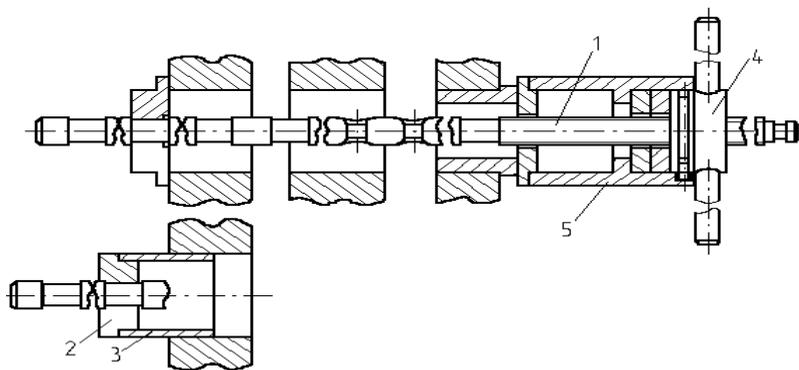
Последовательная запрессовка подшипников-втулок
